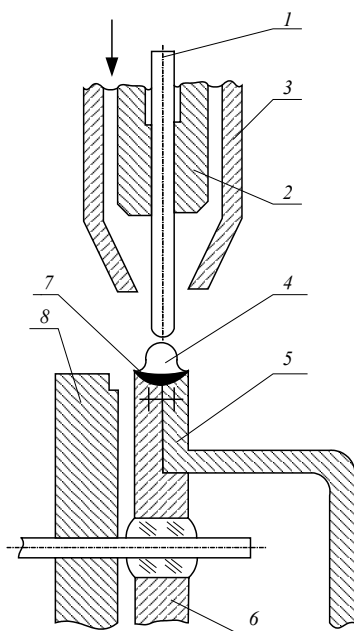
Схема образования сварного соединения при герметизации корпусов аргоно-дуговой сваркой:
